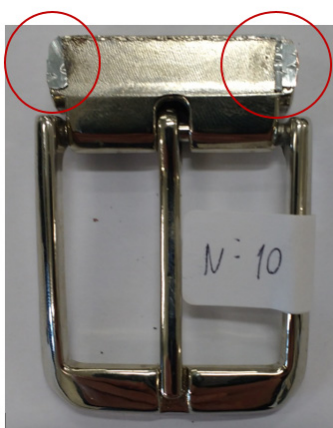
Corte efetuado para facilitar o encaixe da garra inferior.
